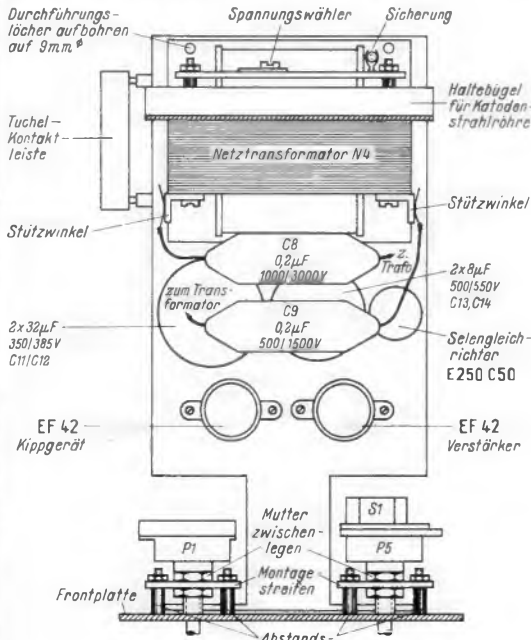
Anordnung der Teile auf dem Chassis, von oben gesehen
